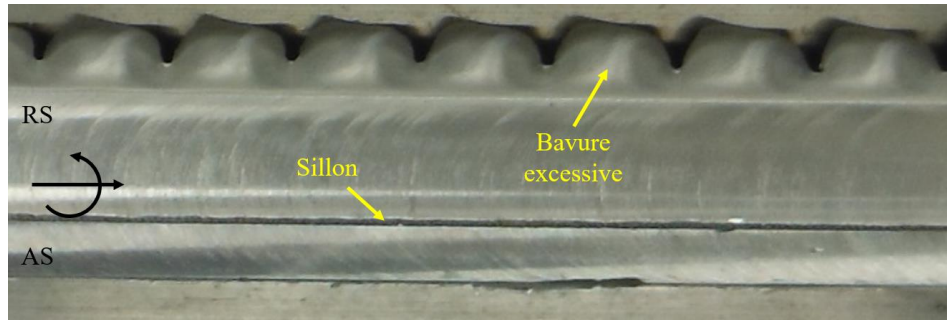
Défauts de surface sur une soudure en 6061-T6
